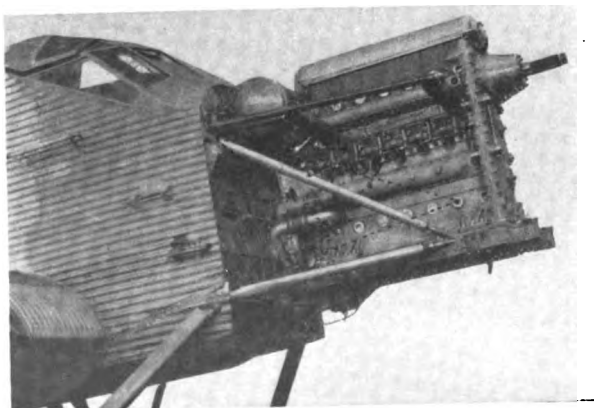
Motor-Aufhängung am Flugzeug-Rumpf.
